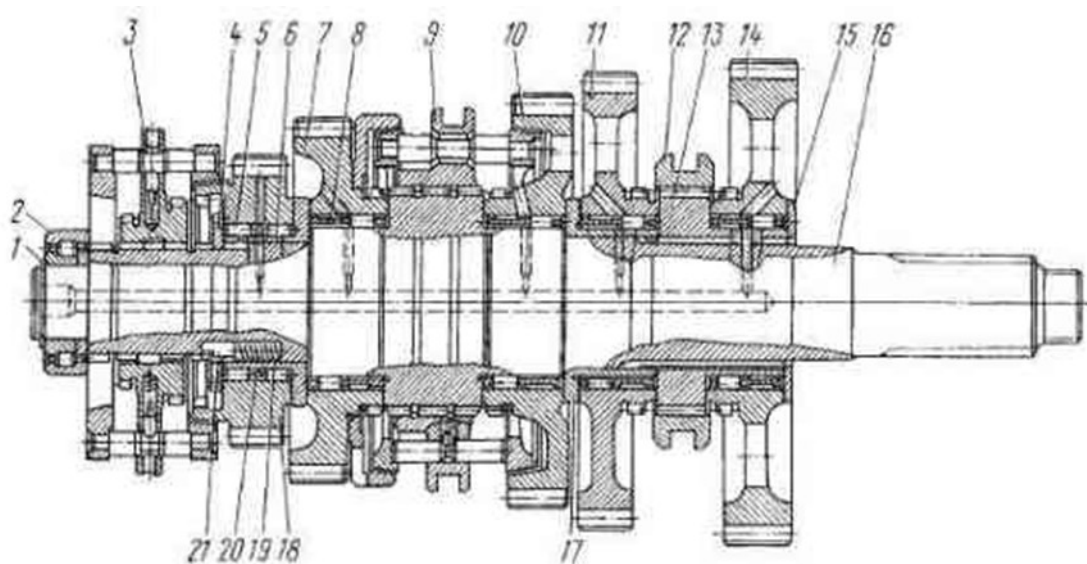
Ведомый вал коробки передач автомобиля Камаз в сборе:
